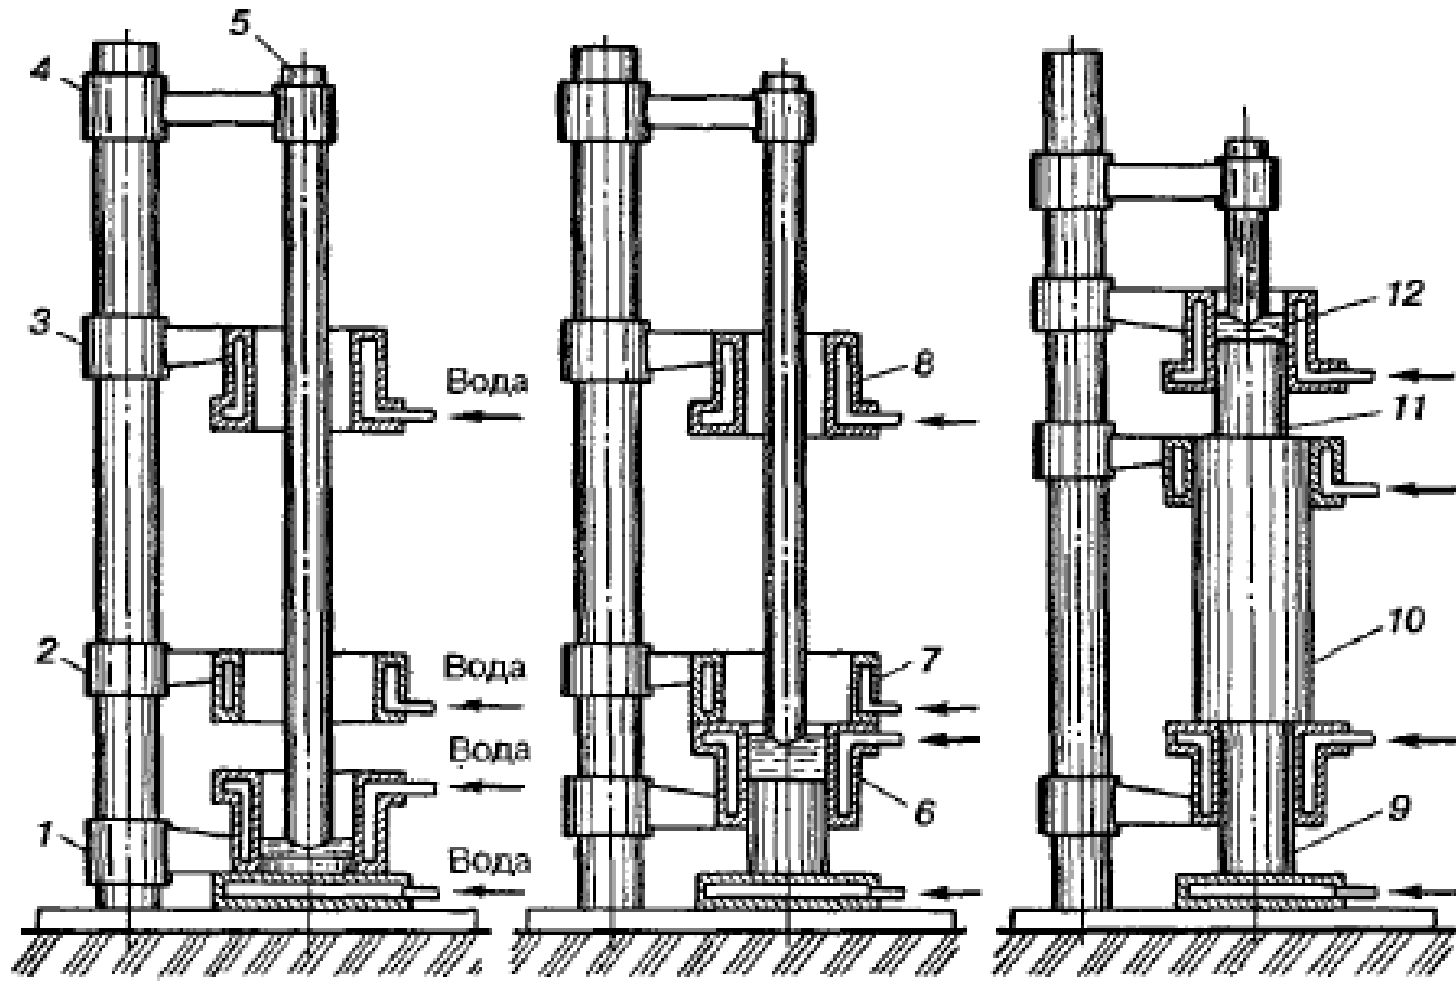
Схеми виготовлення вилівка прокатного валка електрошлаковим виливанням
